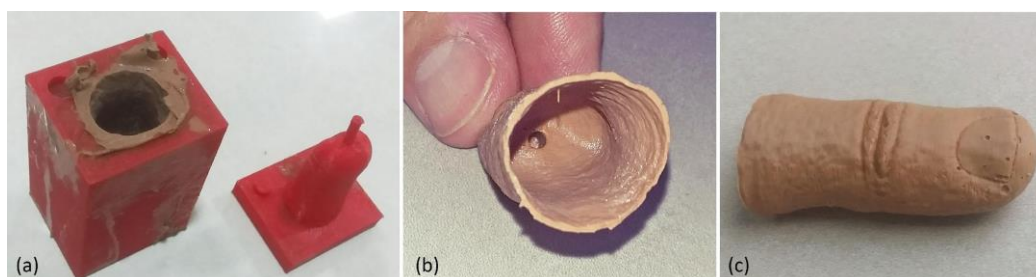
Resultado da moldagem, em (a) molde aberto, em (b) superfície interna, em (c) superfície externa da prótese.
